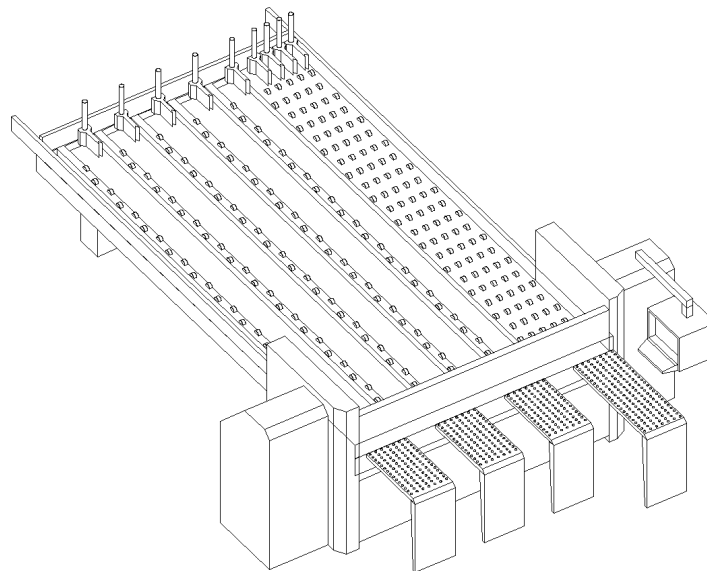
Общий вид форматно-раскроечного центра Holzma
